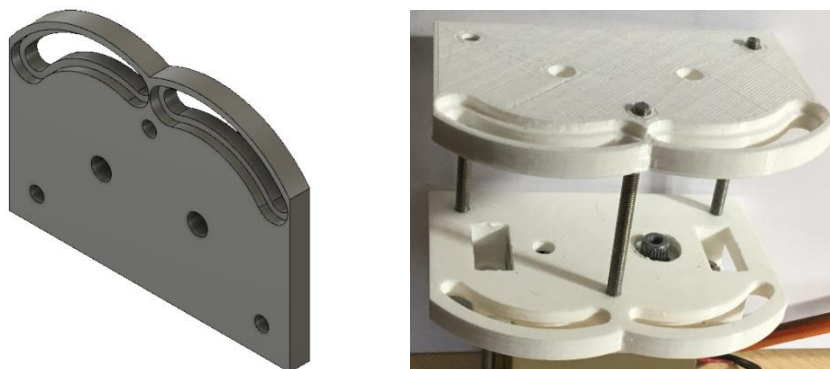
Diseño Cara Superior de Unión y ensamblado junto con Cara Inferior de Unión
